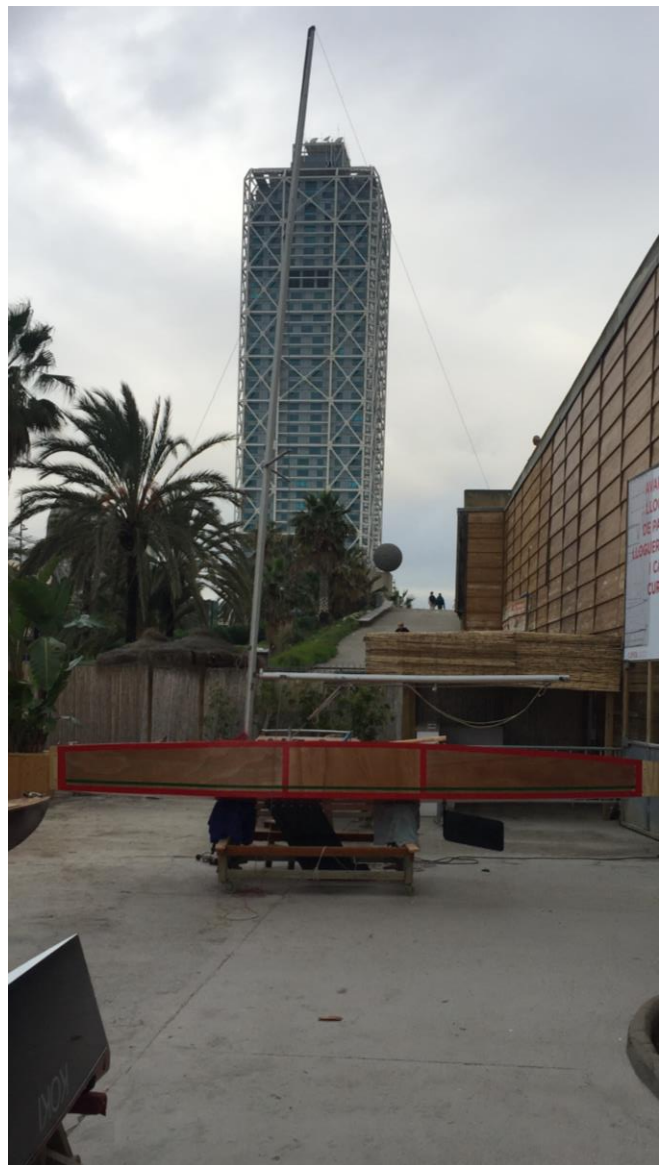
Vista embarcación con arboladura montada (Fuente: Propia)
